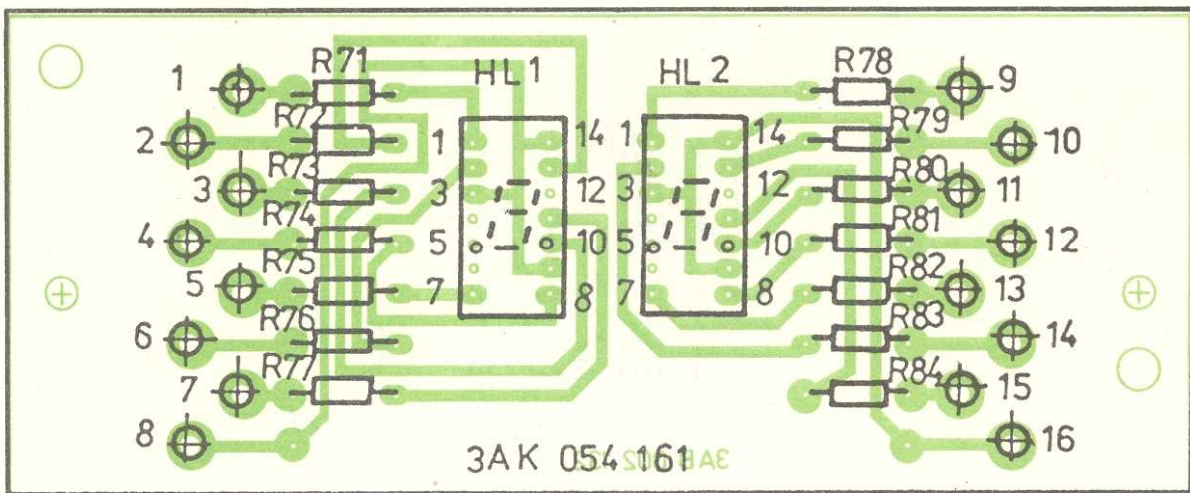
Deska světelných efektů 3AK 054 160 - strana spojů
